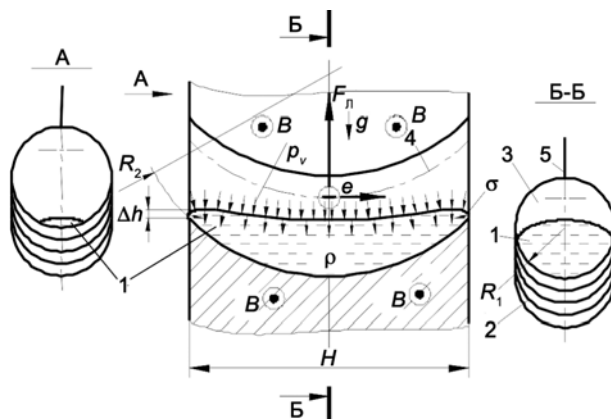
Упрощенная модель канала проплавления при ЭЛС горизонтальным пучком на подъем в присутствии поперечного магнитного поля: 1 – сварочная ванна; 2 – сварной шов; 3 – пароголовый канал; 4 – ось пучка; 5 – стык
